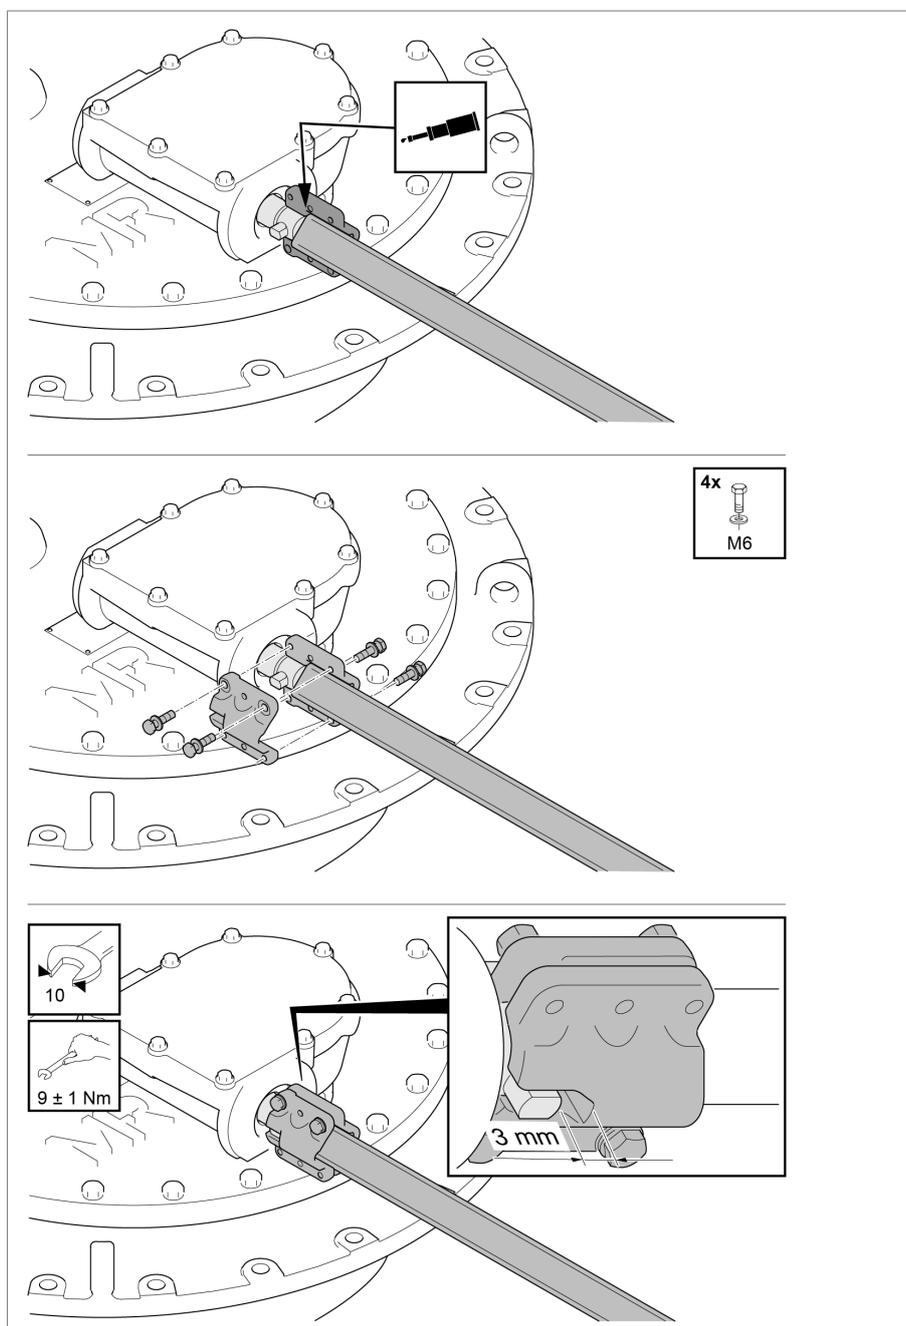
Крепление четырехгранной трубы на верхнем редукторе
